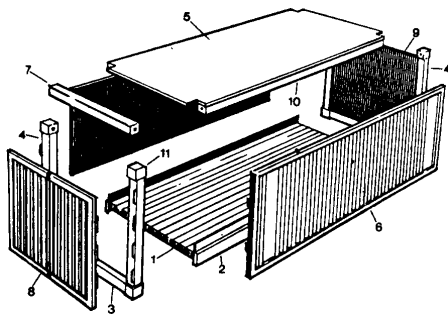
Vista detallada del diseño y de la construcción del contenedor
